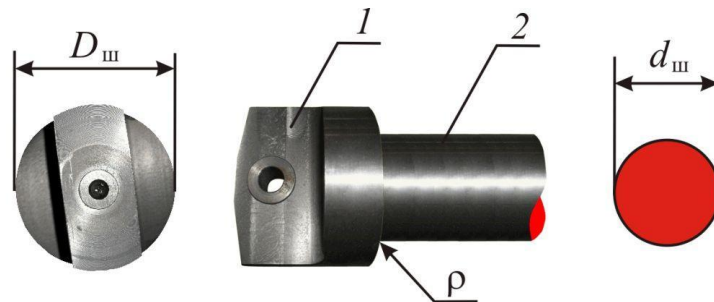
Шпиндель: 1 - головка з лопаттю ; 2 – вал
